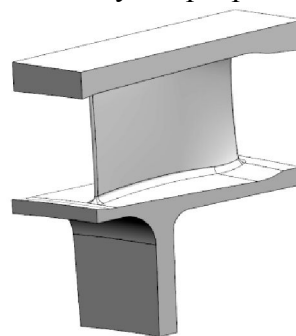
3D-модель отливки лопатки статора компрессора 15 ступени
